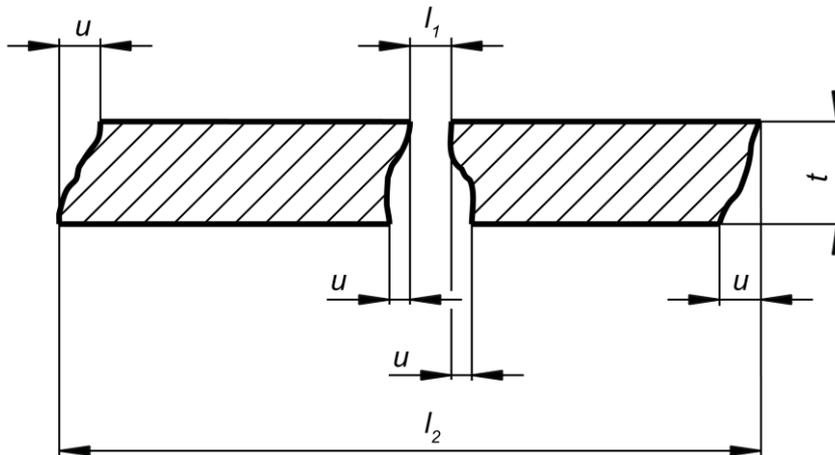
Termes applicables à la fente de coupe et à la surface de coupe
